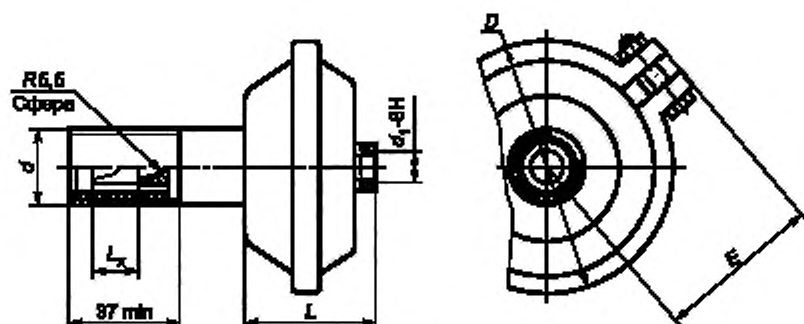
Тормозная камера с резьбовой трубой для крепления непосредственно на тормозном механизме
